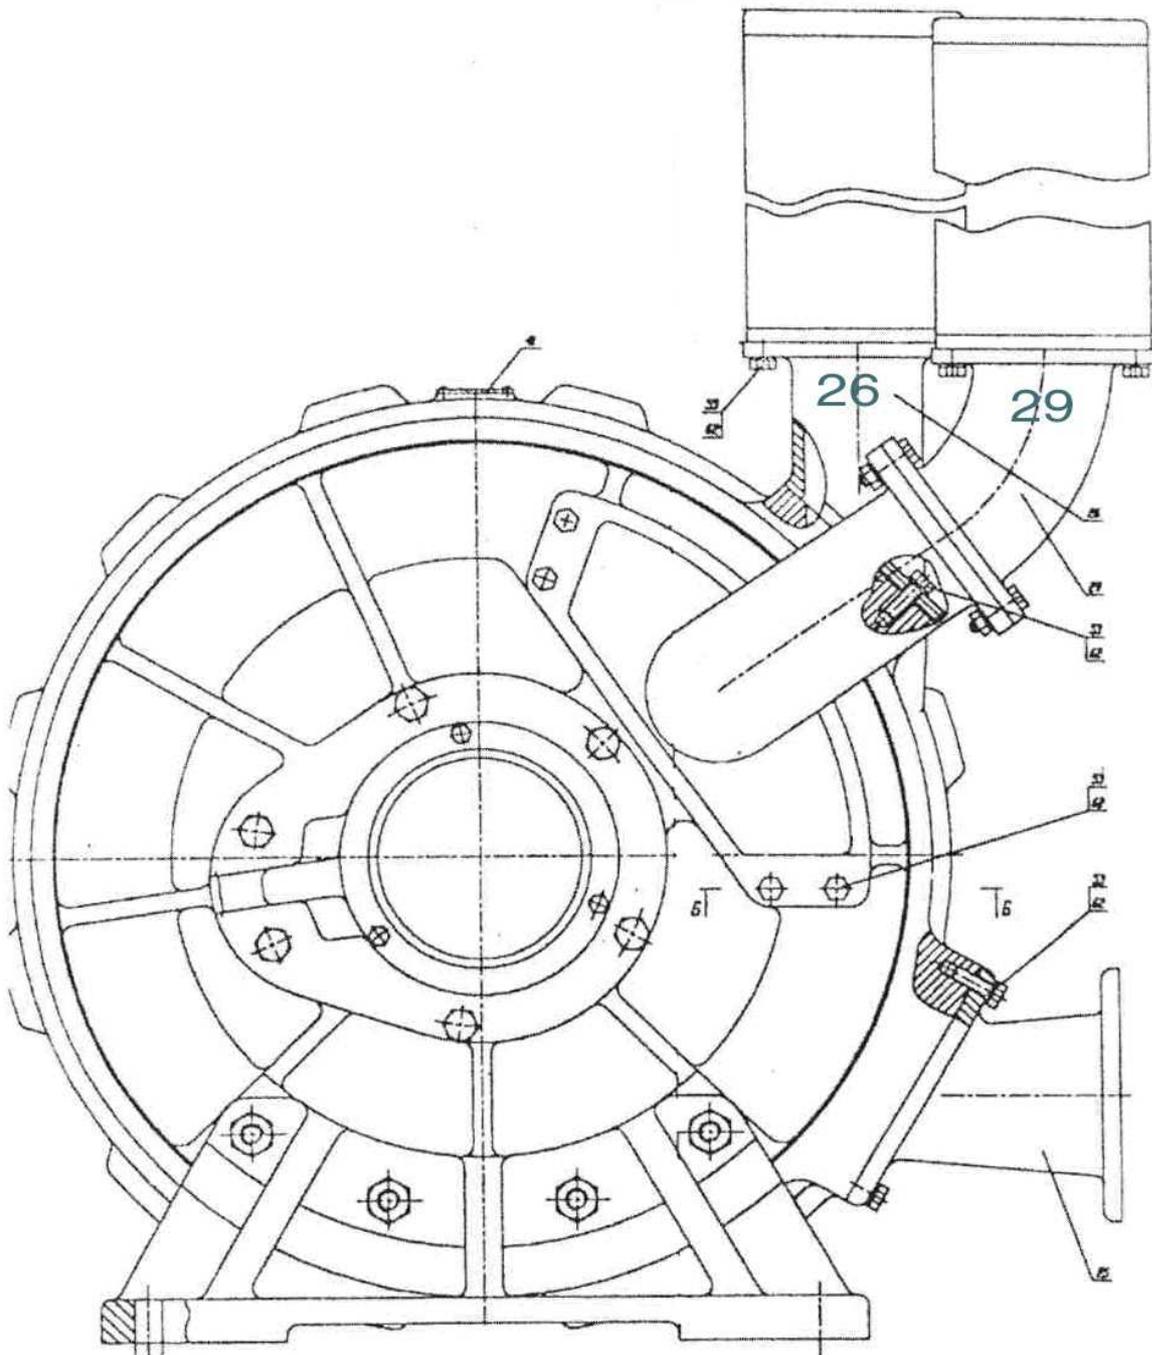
Сборочный чертеж компрессора. Вид сбоку.
